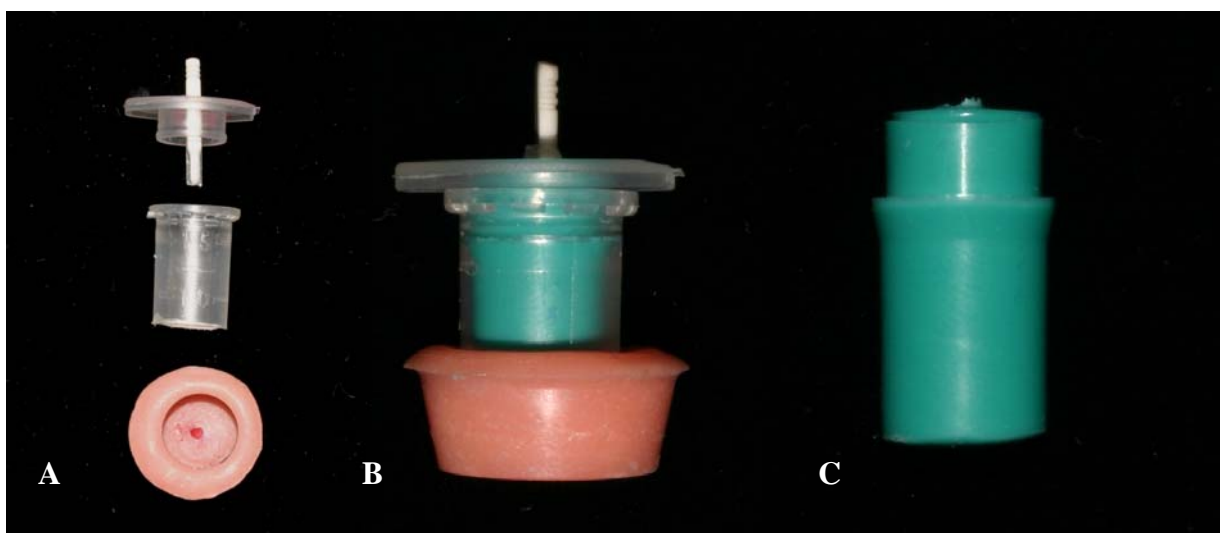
(A) Dispositivo confeccionado para a moldagem do pino, (B) moldagem do pino e (C) a matriz de silicone de reação de adição.
